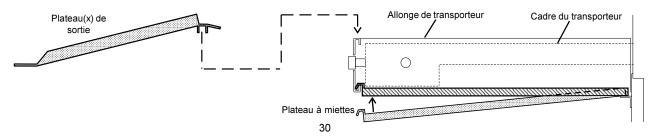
Assemblage final - Plateau(x) de sortie et plateaux à miettes
